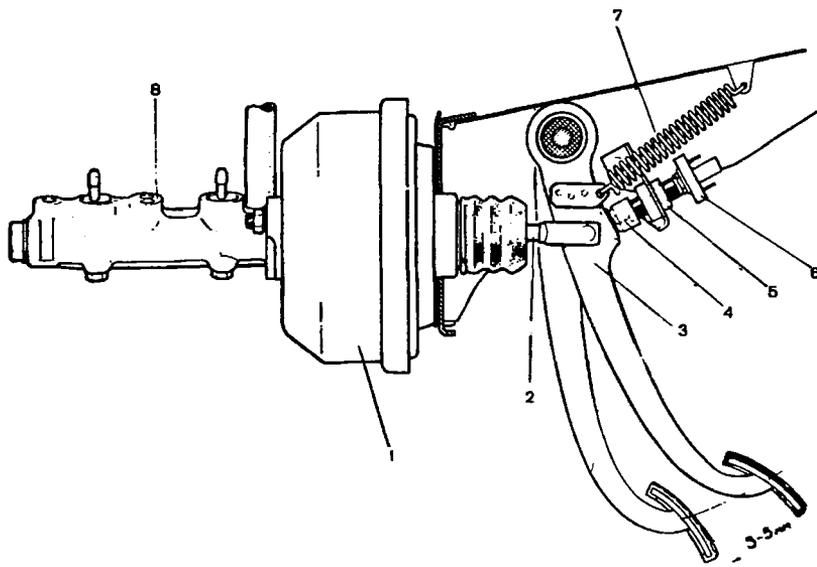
Педаль тормоза: 1 - вакуумный усилитель; 2 - толкатель; 3 - педаль тормоза; 4 - буфер выключателя стоп-сигнала; 5 - гайка выключателя; 6 - выключатель стоп-сигнала; 7 - оттяжная пружина педали; 8 - главный цилиндр
